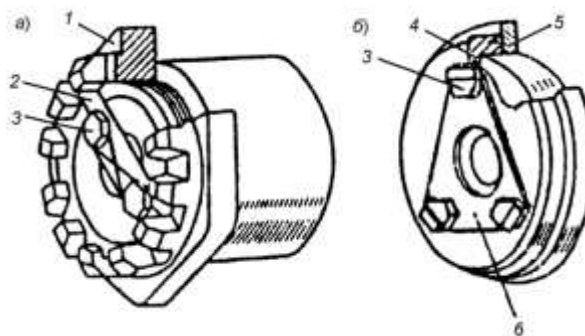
Варианты торцевого крепления подшипников на шейке оси:
